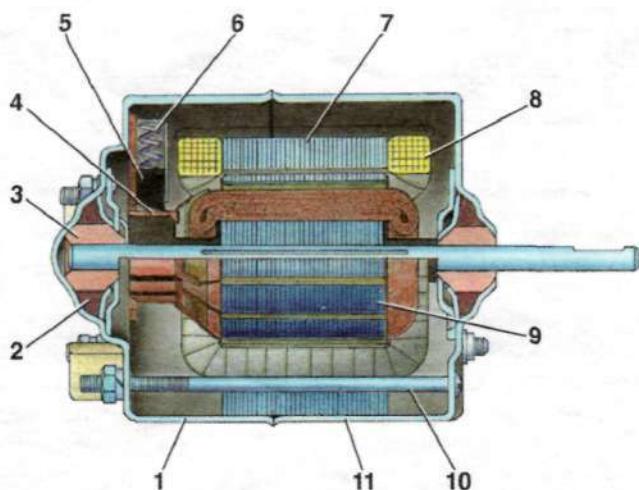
Электродвигатель МЭ218 вентилятора отопителя. 1. Крышка. 2. Фетровое кольцо. 3. Металлокерамический подшипник. 4. Коллектор. 5. Щетка. 6. Пружины щетки. 7. Поляр статора. 8. Катушка обмотки возбуждения. 9. Якорь. 10. Стяжной винт. 11. Корпус.
